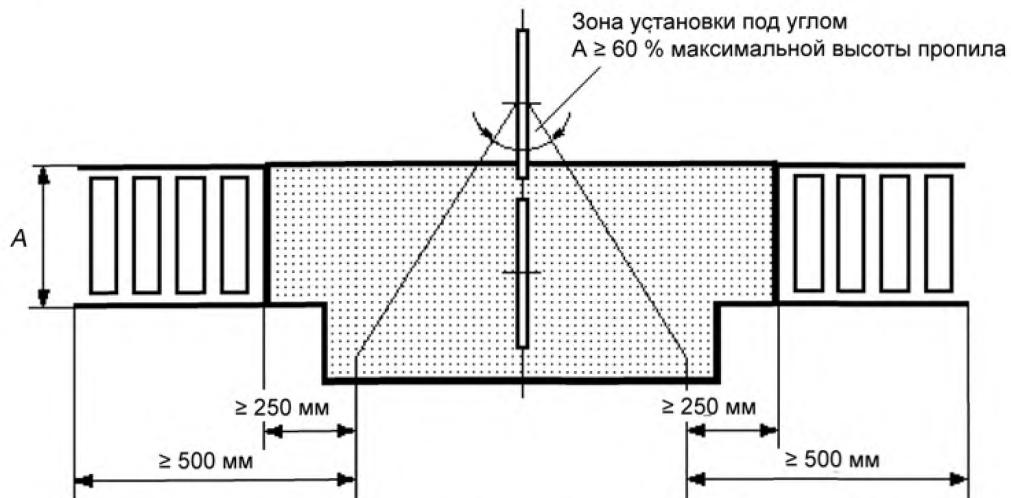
с) – Опорная поверхность для обрабатываемой заготовки в станках с ручным обслуживанием и в станках-полуавтоматах с диаметрами дисковой пилы ≤ 315 мм
